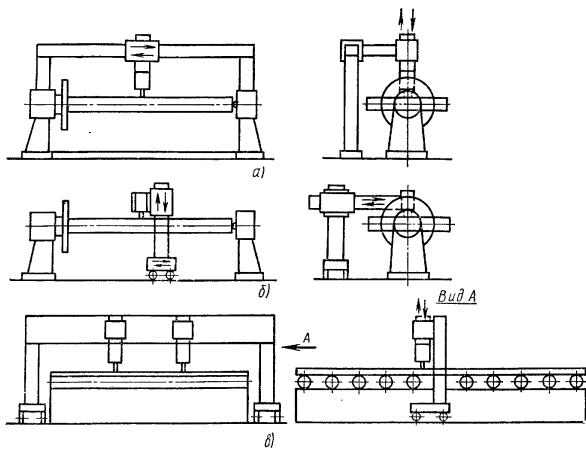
Типовые схемы компоновки установок для сварки прямолинейных швов изделий типа балок и рам
